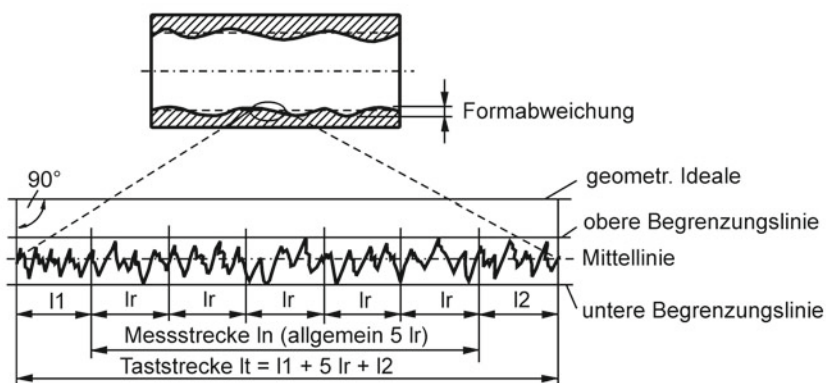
Taststrecke, Messstrecke und Einzelmessstrecken zur Erfassung der Oberflächenkennwerte
